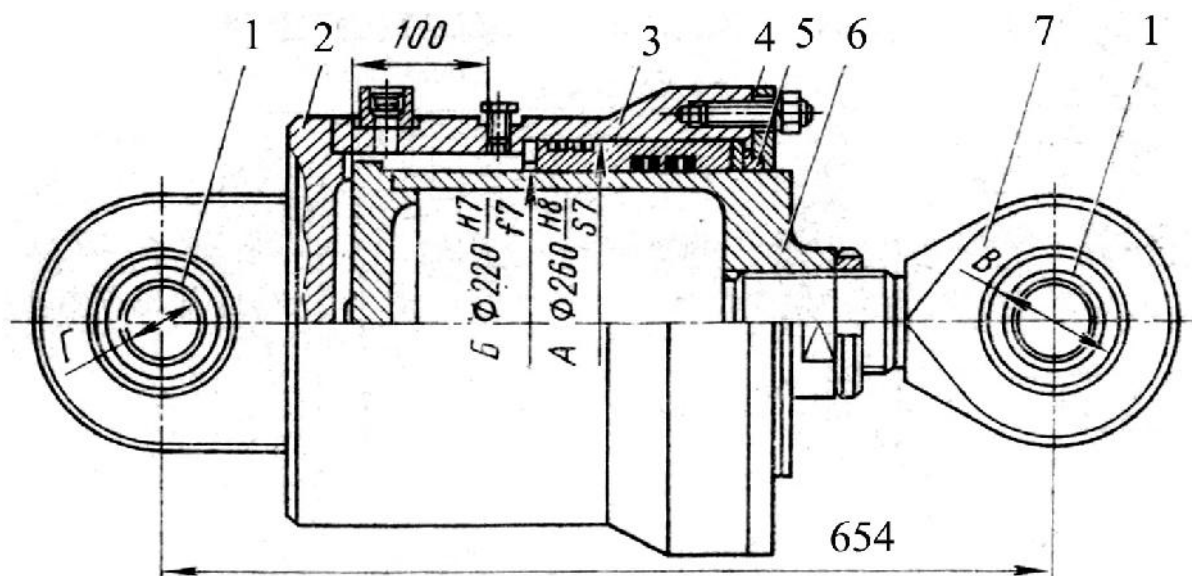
Плунжерный гидроцилиндр: 1 – втулка; 2 – крышка; 3 – цилиндр; 4 – грязесъемник; 5 – сальник; 6 – плунжер; 7 – проушина
